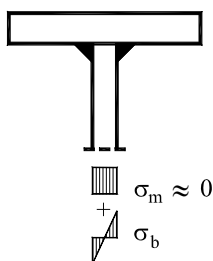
Anschluß Steg – Flansch, Kerbdetail und Beanspruchung
